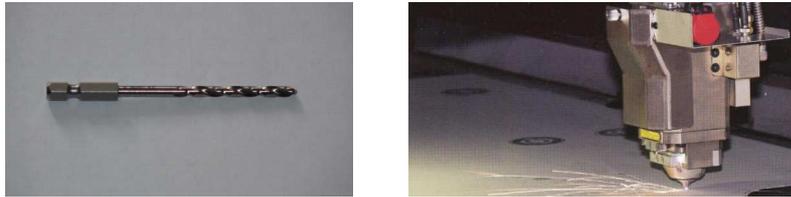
Die mechanische Wechselwirkung zwischen einem Bohrer und dem Werkstück führt zu physikalischen Widersprüchen, die beim Laserbohren entfallen.
